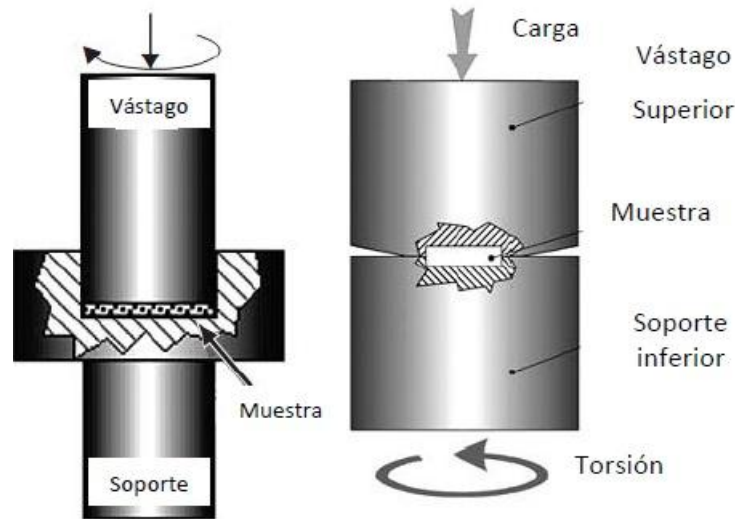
Dibujo esquemático de la técnica de presión en alta torsión [29].
